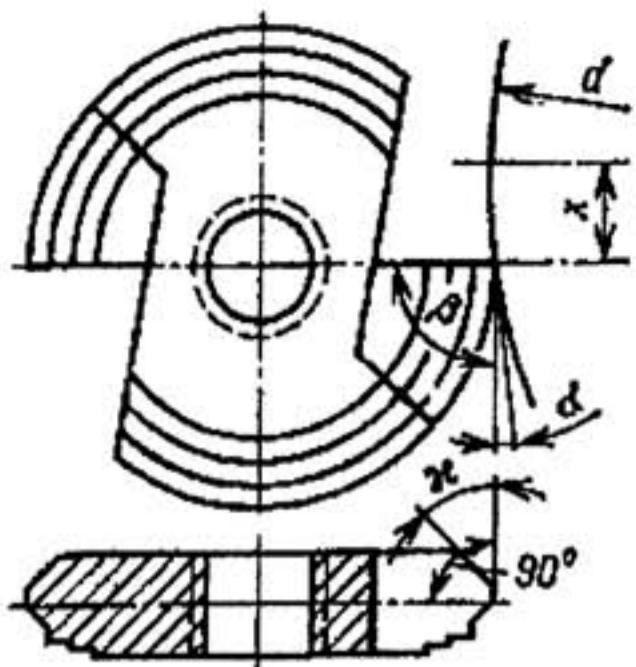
Круглый фасонный инструмент (установка оси инструмента ниже оси заготовки обеспечивает создание заднего угла α)
